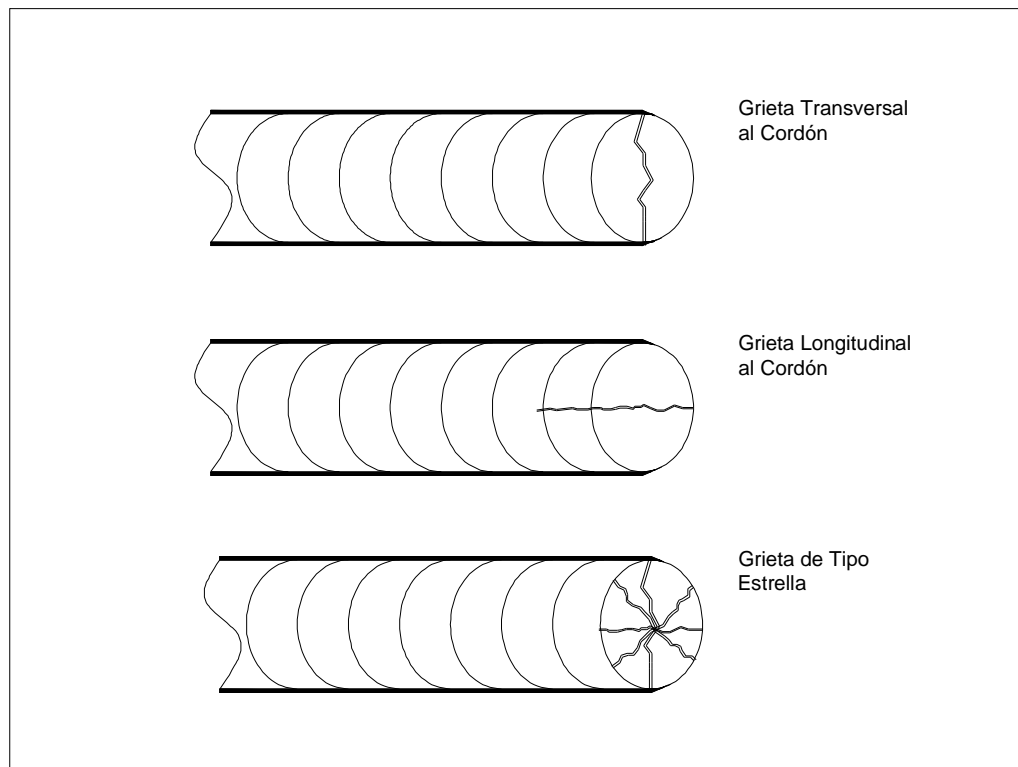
Tres tipos básicos de agrietamiento en cordones de soldadura (SOLDADURA, APLICACIONES Y PRACTICAS, Henry Horwitz, P.E.1997, capítulo22, Pág. 692).
